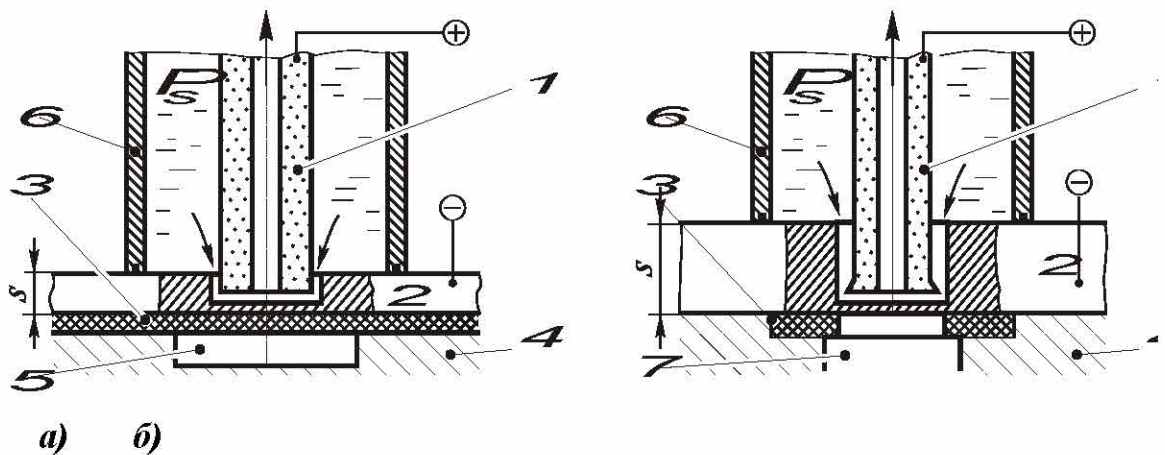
Формоутворення отворів: а – при малій товщині заготовки; б – при значній товщині заготовки
